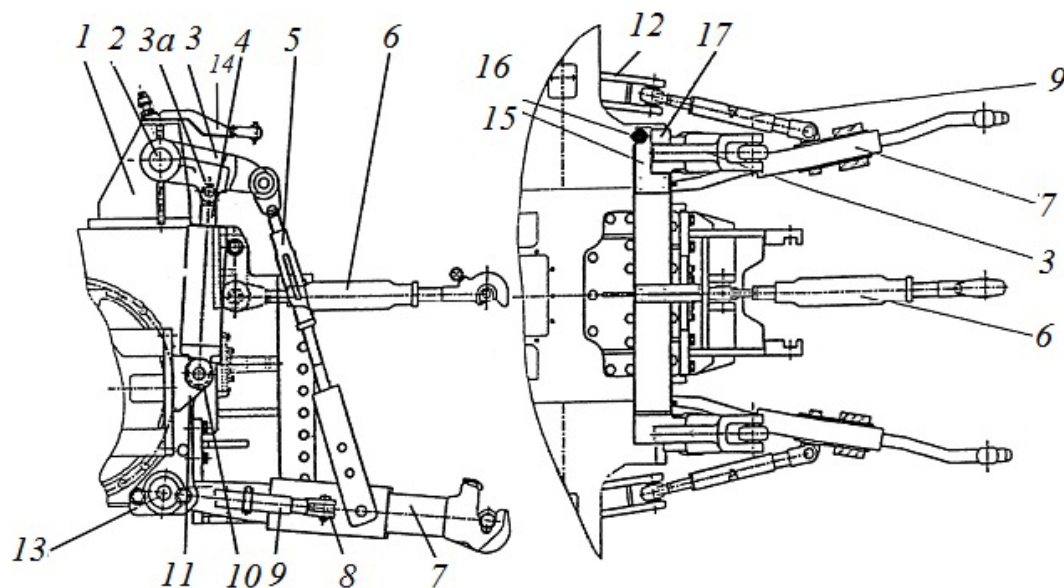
Заднее ПНУ «Беларус-2522»: 1 – кронштейн поворотного вала; 2 – поворотный вал; 3 – наружные рычаги (левый и правый); 3а – пальцы штоков гидроцилиндров; 4 – гидроцилиндры; 5 – раскосы; 6 – верхняя тяга; 7 – нижние тяги; 8 – проушины; 9 – стяжки; 10 – пальцы; 11 – гидроцилиндры и кронштейны нижних тяг; 12 – кронштейны стяжек; 13 – пальцы (силовые датчики); 14 – кронштейн крепления верхней тяги; 15 – кронштейн датчика позиционного; 16 – датчик позиционный; 17 – эксцентрик
